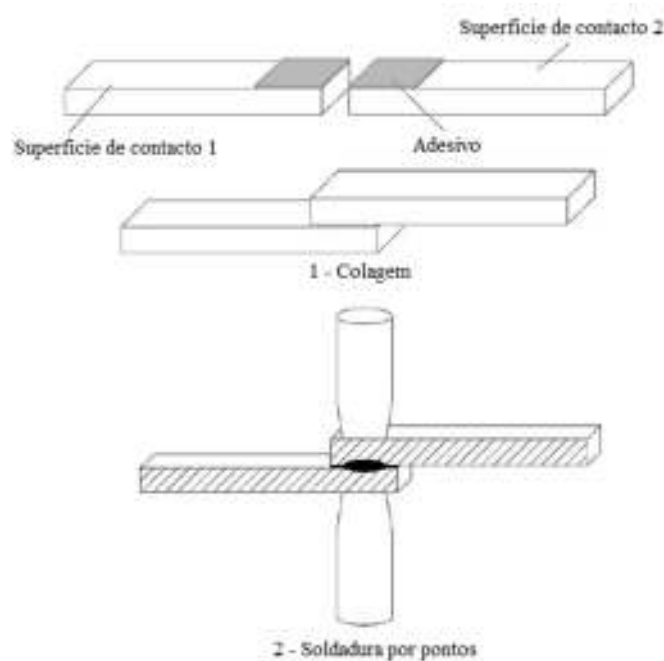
Processo ligação de juntas adesivas-soldadas através da técnica "weld-through" [52].
